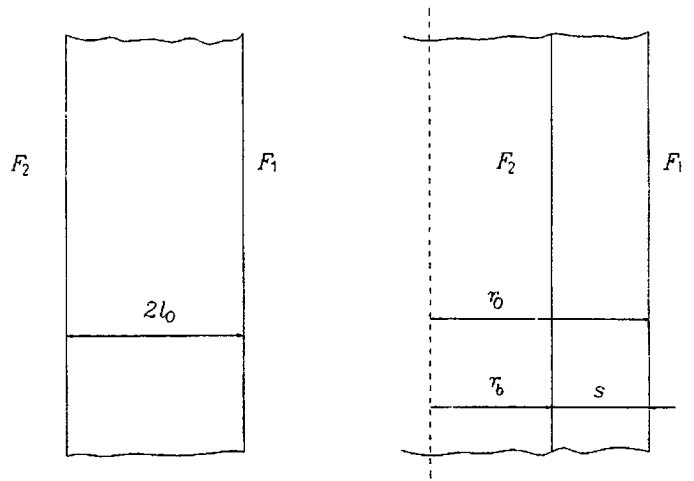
Схемы для сравнения плоской и полый цилиндрической отливки
